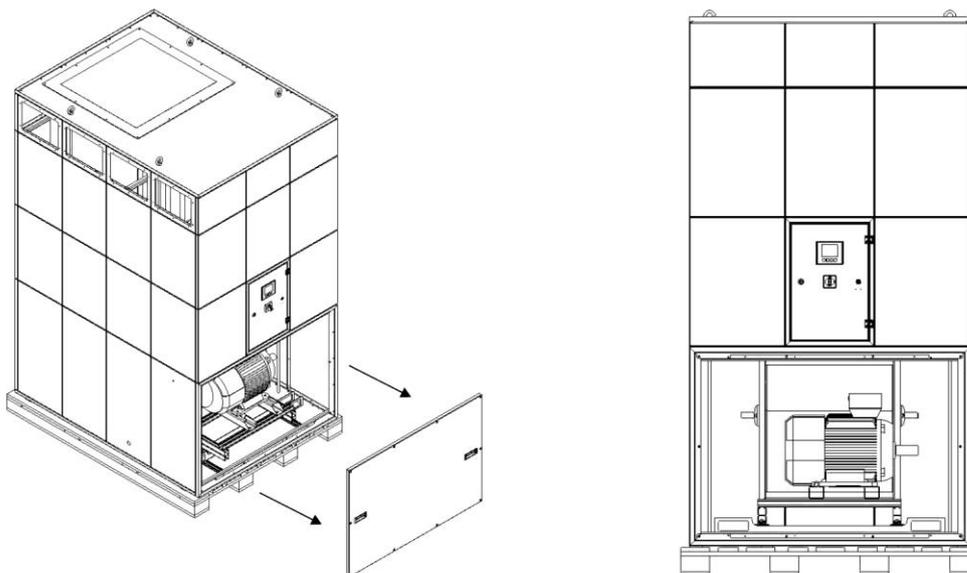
ouverture de la porte de maintenance de la section du ventilateur
